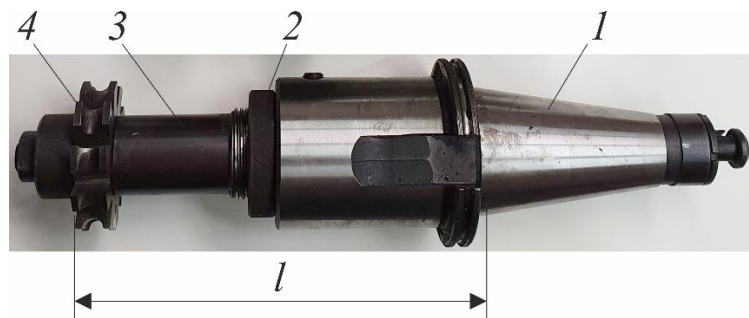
АСП для фрезерования дисковыми фрезами: 1 - хвостовик базисного агрегата; 2 - регулировочная гайка 3 – рабочая часть сменного агрегата; 4 – дисковая фреза;
